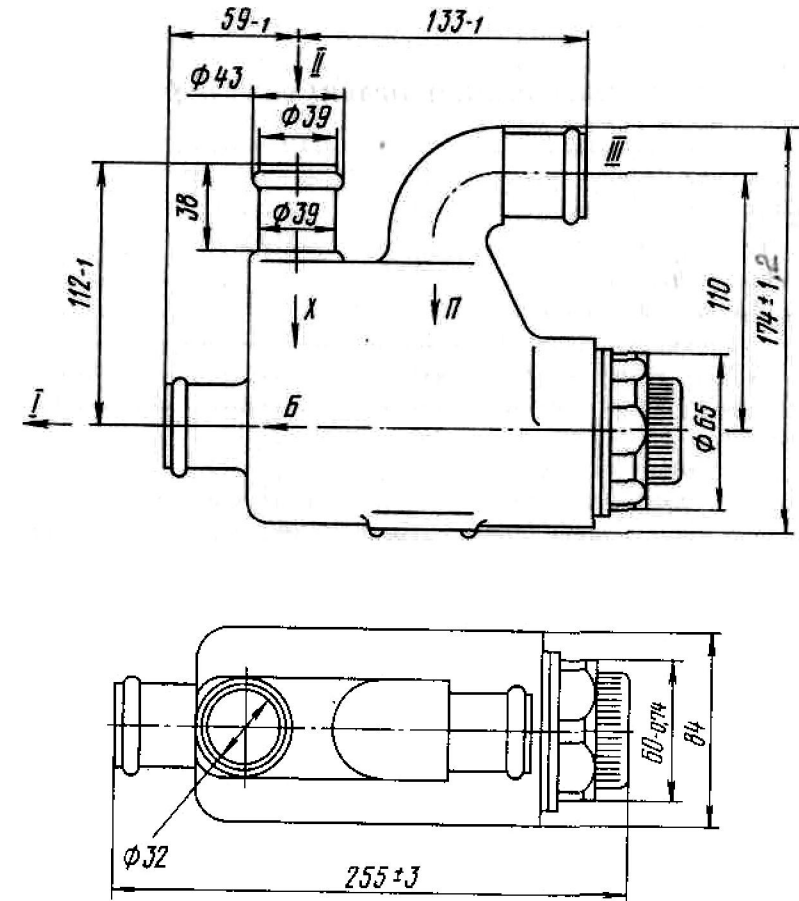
Габаритные и присоединительные размеры терморегулятора:
